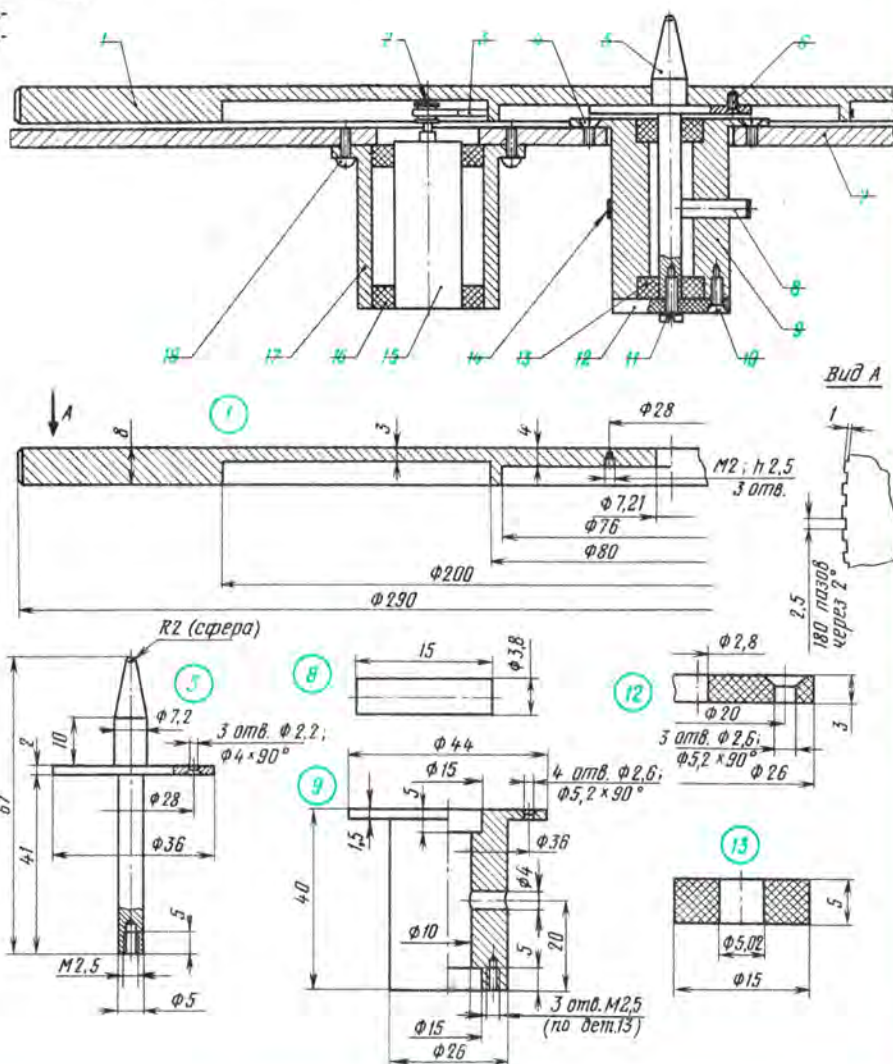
Узел привода диска и его основные детали: 1 — диск, Д16-Т, закрепить на дет. 5 винтами 6; 2 — шкив-насадка, ЛС59-1; 3 — пассив резиновый; 4 — винт М2,5×5, 4 шт.; 5 — валик, Ст. 45, калибр НRC48... 52, рабочие поверхности шлифовать; 6 — винт М2×4, 3 шт.; 7 — панель проигрывателя, Д16-Т толщиной 4 мм; 8 — штифт, капролон В; 9 — втулка, Д16-Т, закрепить на дет. 7 винтами 4; 10 — винт М2,5×8, 3 шт.; 11 — винт М2,5×8; 12 — подпятник, капролон В, закрепить винтами 10; 13 — подшипник, капролон В, 2 шт.; 14 — кольцо резиновое; 15 — электродвигатель ДПР-2-Ф1-13, закрепить в стакане 17 кольцами 16; 16 — кольцо, резина НО66-1, клеить к дет. 15 и 17 клеем 88-Н; 17 — стакан, Д16-Т, закрепить на дет. 7 винтами 18; 18 — винт М2,5×6, 3 шт.
